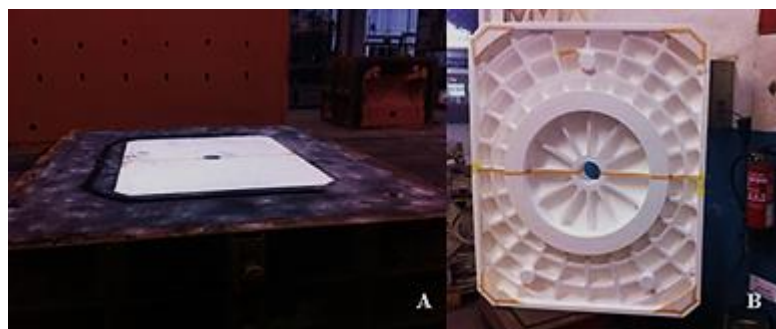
moldação pronta a aplicar o R-limoneno.
